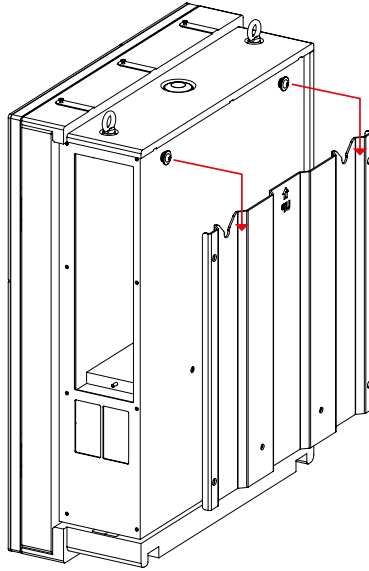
Wall Box deslizándose sobre la placa de montaje
